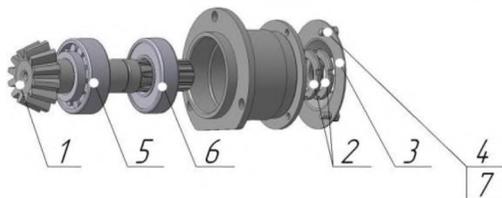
Узел ведущей шестерни УМДУ-80/82.02.04
